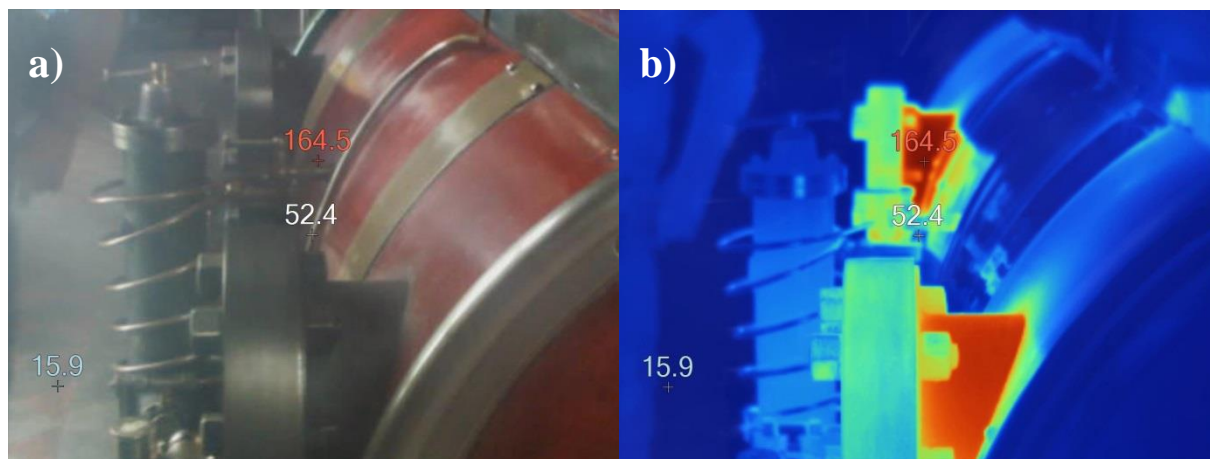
a) Imagem real da máquina b) Imagem térmica da máquina
